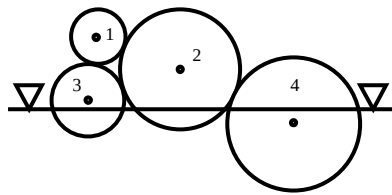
Относительное расположение зубчатых колес и масляной ванны коробки передач. 1 – входной вал; 2 – выходной вал; 3 – реверсный вал; 4 – дифференциальный вал
